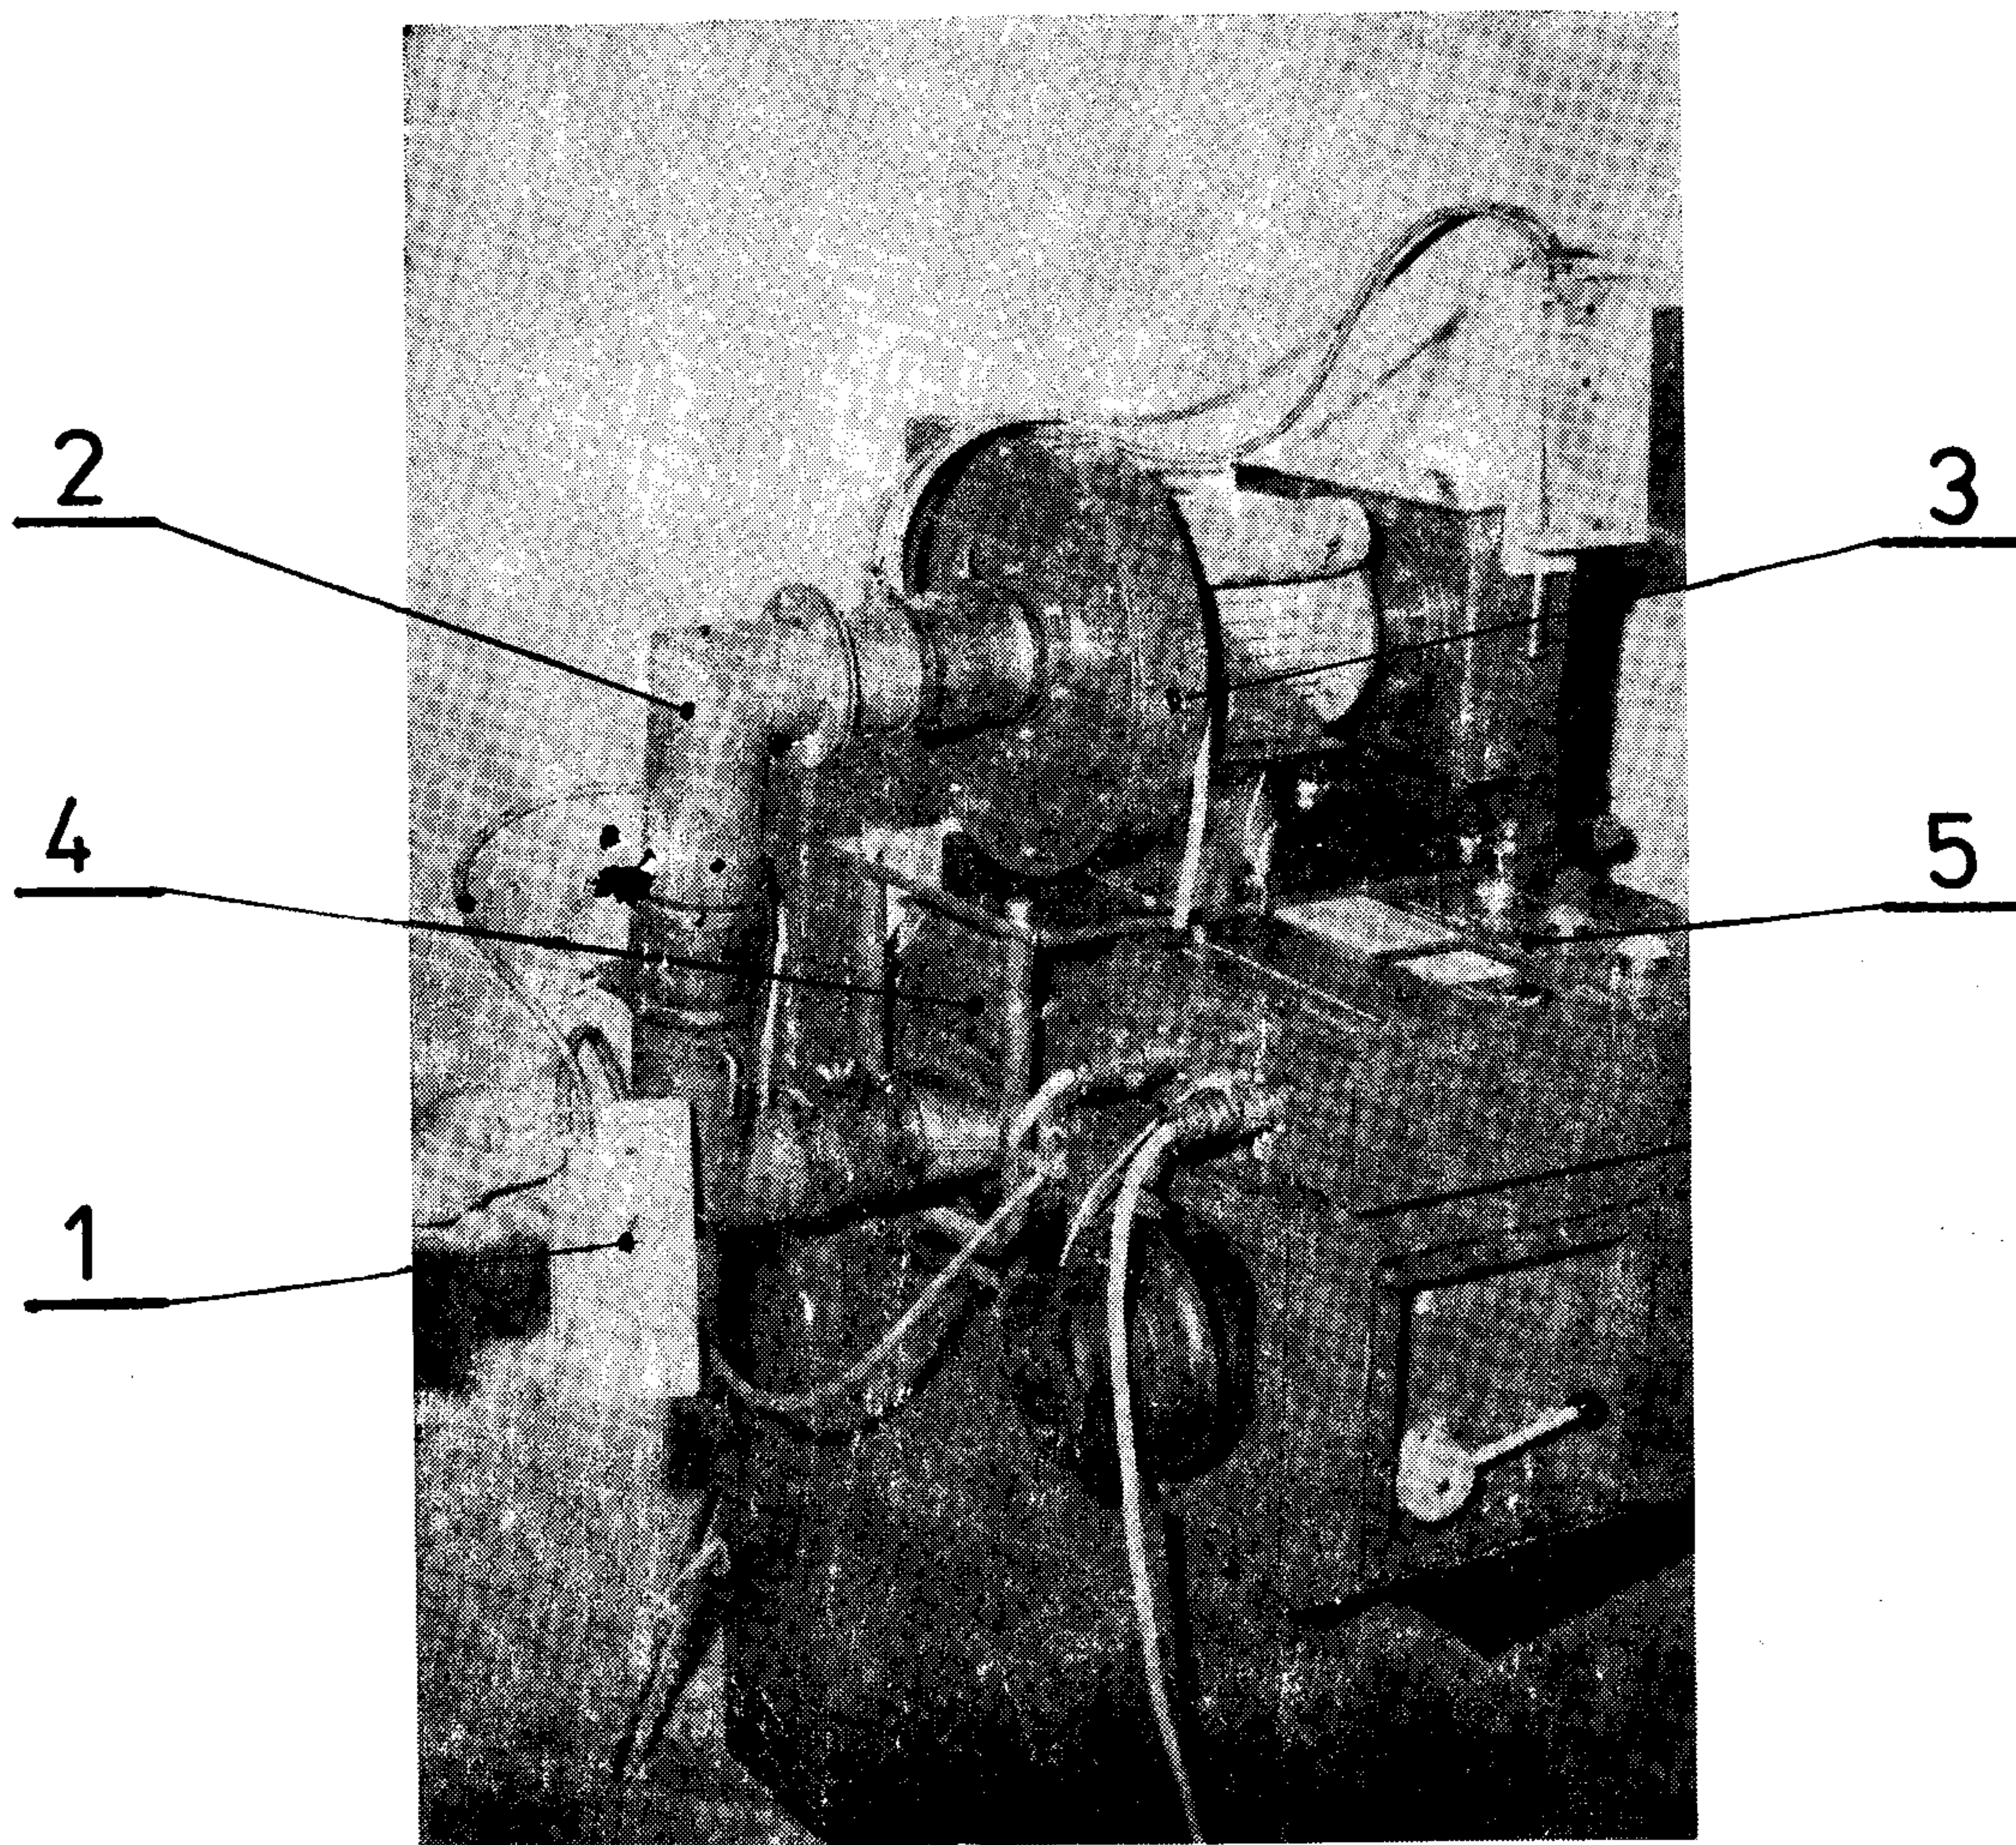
Montáž třetí a čtvrté montážní podskupiny:
